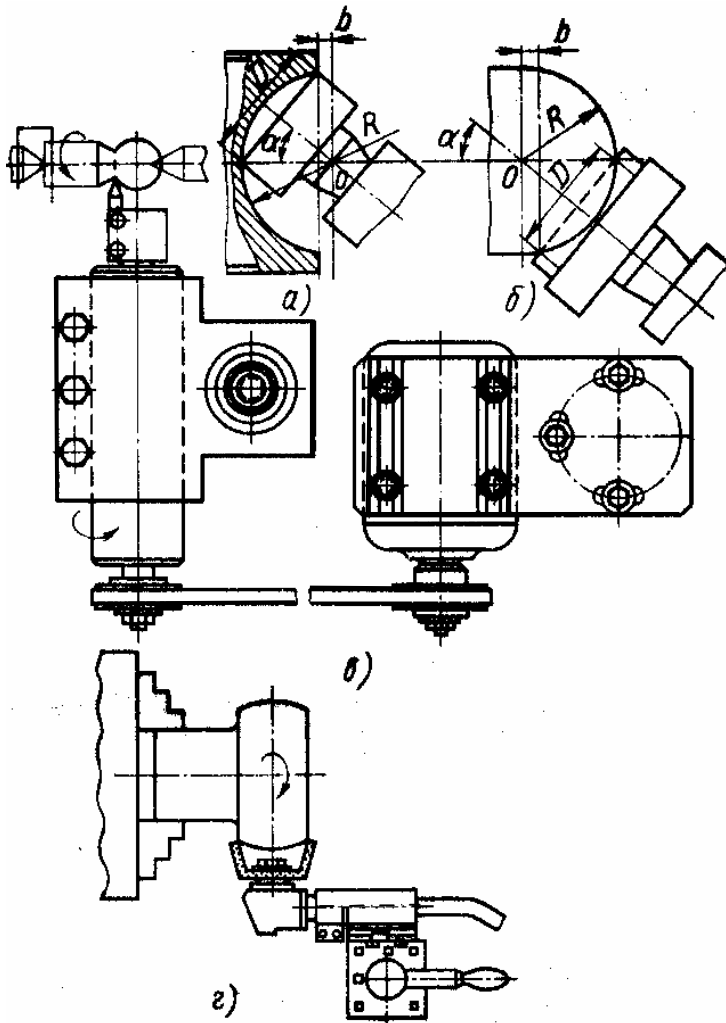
Схеми обробки сферичних поверхонь заготовок чашковими інструментами
